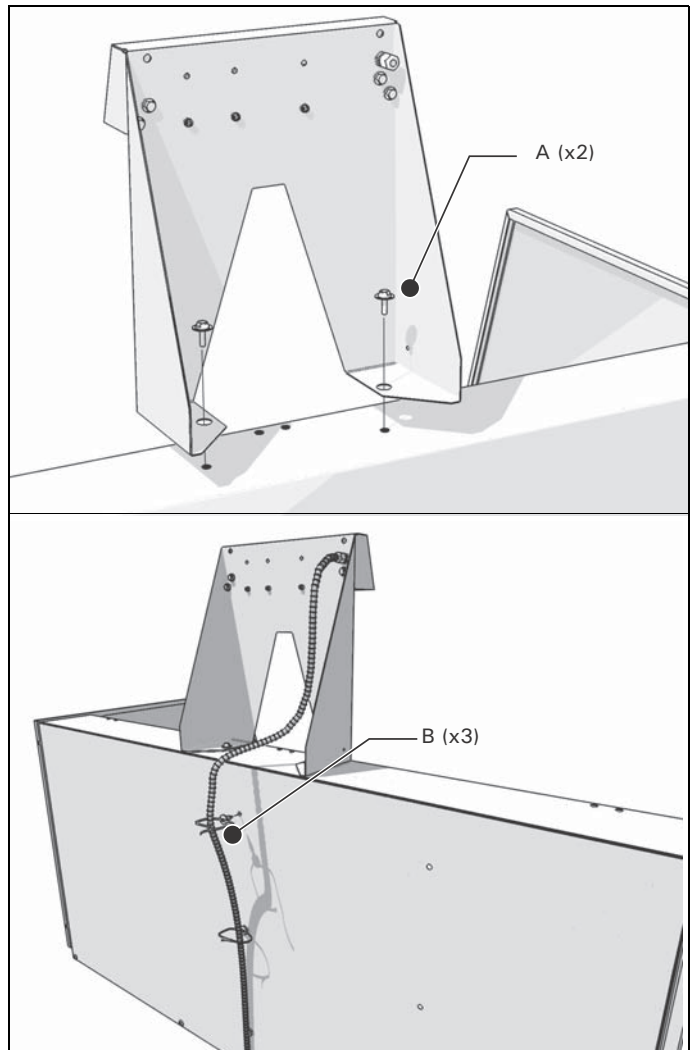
Montage du détecteur de mouvements (vue de derrière)
